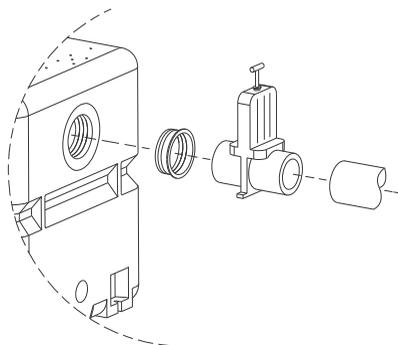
Anschließen einer Zulaufleitung mit Absperrventil
